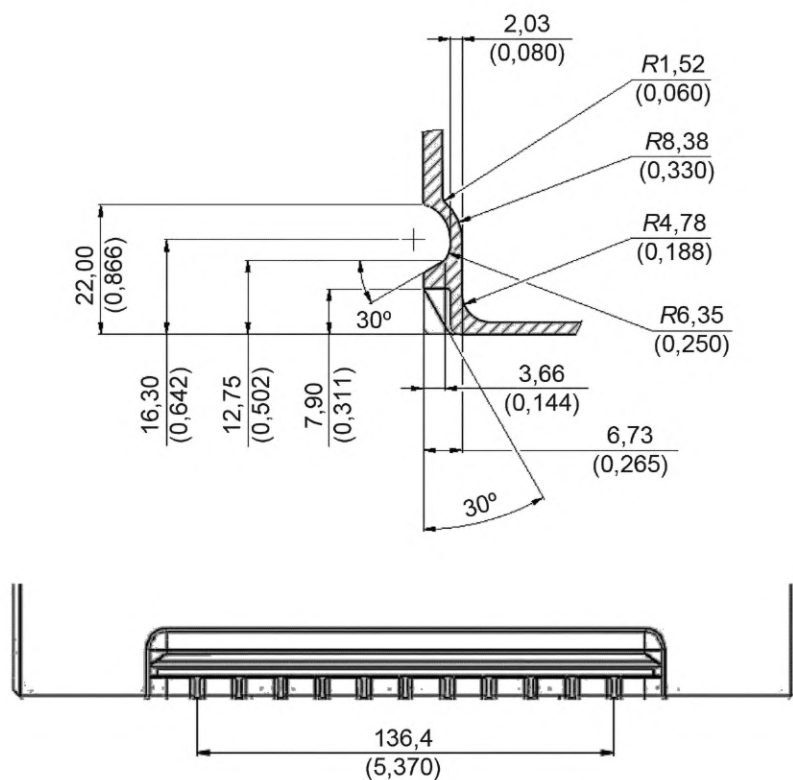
Форма и размеры углублений на корпусе, образующих бортик на короткой стороне корпуса батареи
